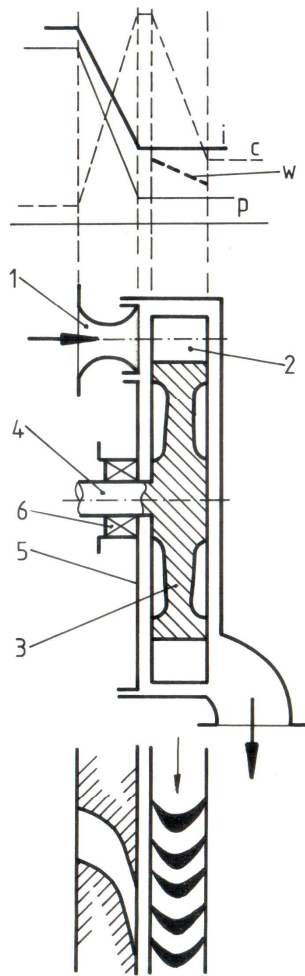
Turbina cu o treaptă de presiune și viteză: 1 - ajutoraj Laval; 2 - palete pe rotor; 3 - disc; 4 - arbore; 5 - carcasă; 6 - etanșări
